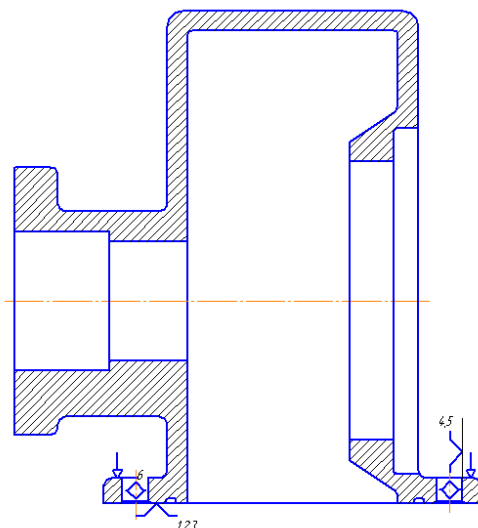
Теоретична схема базування на фрезерній та свердлильній операціях
